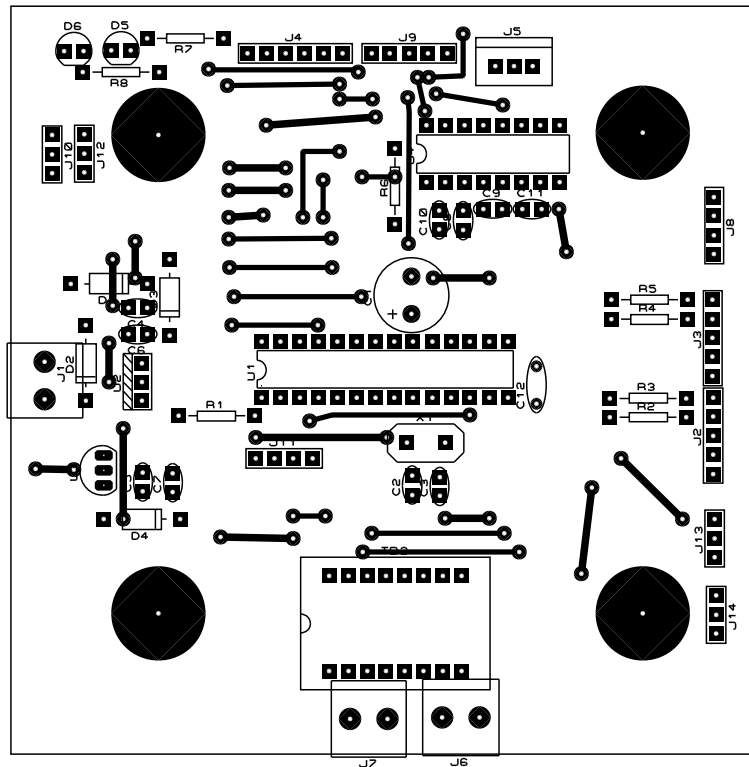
Vista superior de la plaqueta electrónica construida para la concreción del trabajo.
